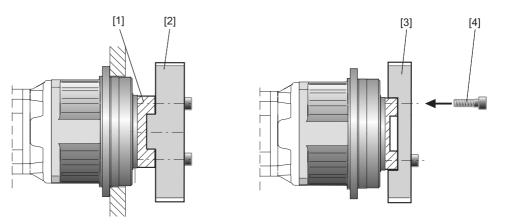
Exemplo de montagem PSBF.. – cubo flangeado
